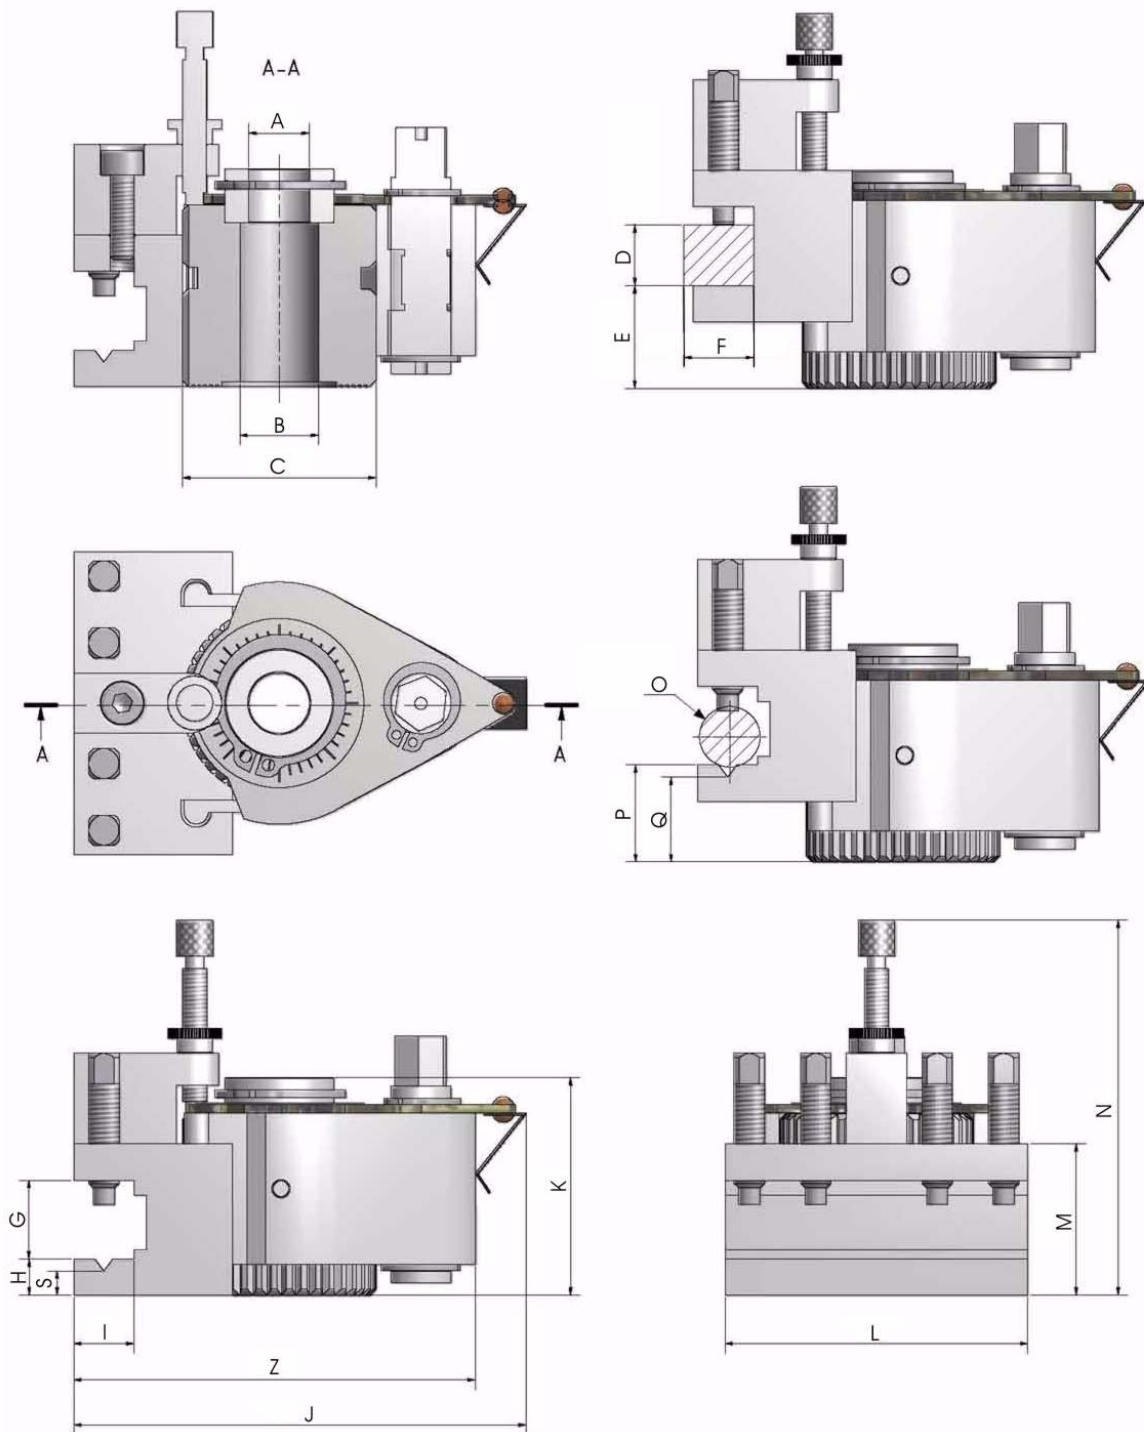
Stahlhalter für Vierkantmeißel/ Rundmeißel - Tool holder for square tool/ round tool
